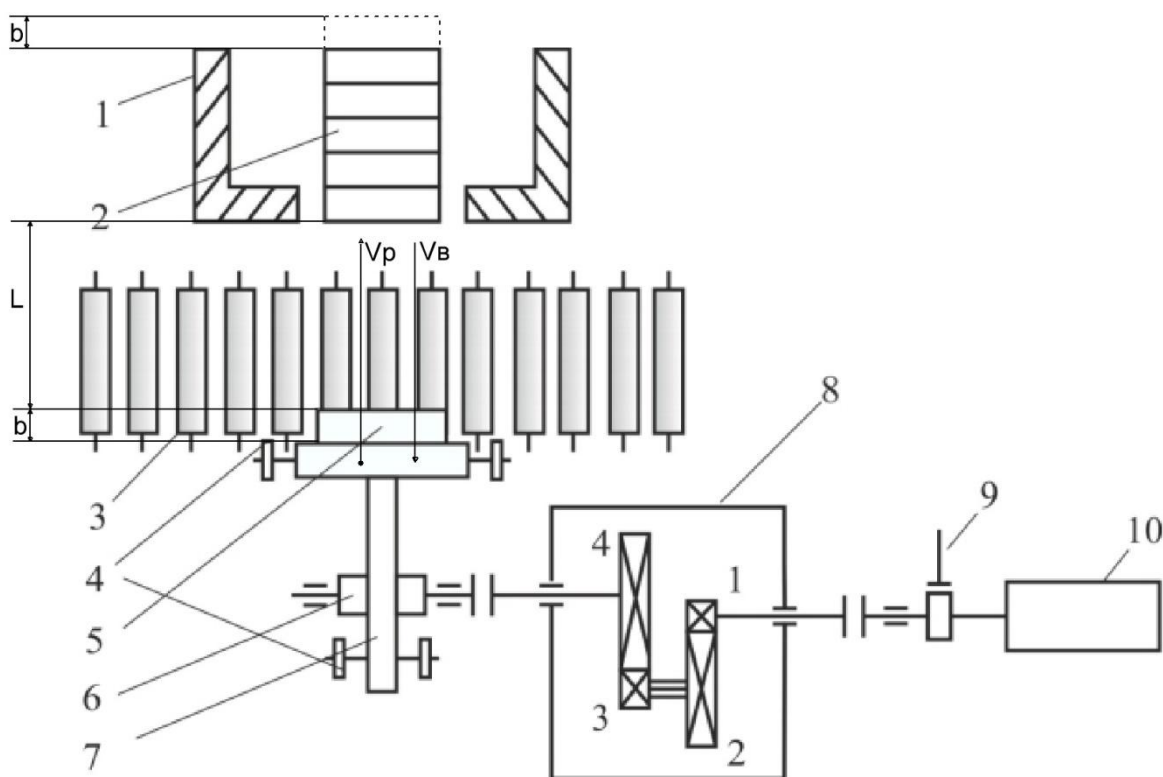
Кинематическая схема передвижения: 1 –печь; 2 – заготовки в печи; 3– подающий рольганг; 4 – опорный ролик; 5– заготовка; 6 – реечная шестерня; 7 – толкатель; 8 – редуктор; 9 – тормозной шкив; 10– электродвигатель
